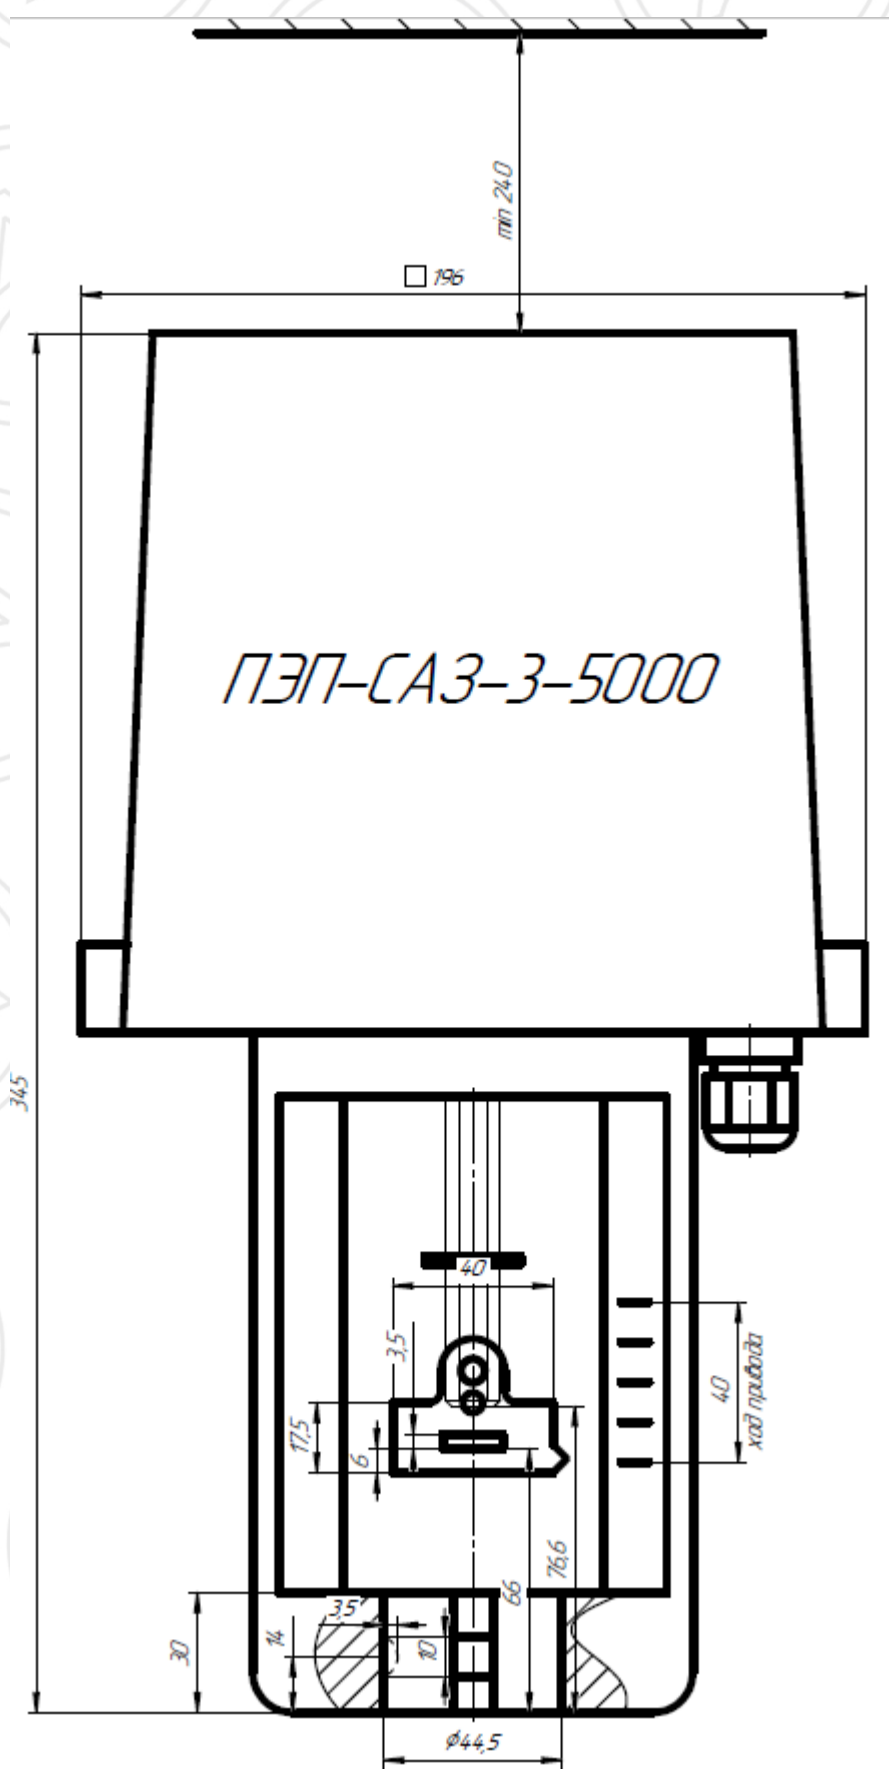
Габаритные и присоединительные размеры ПЭП-СА3-3-5000
